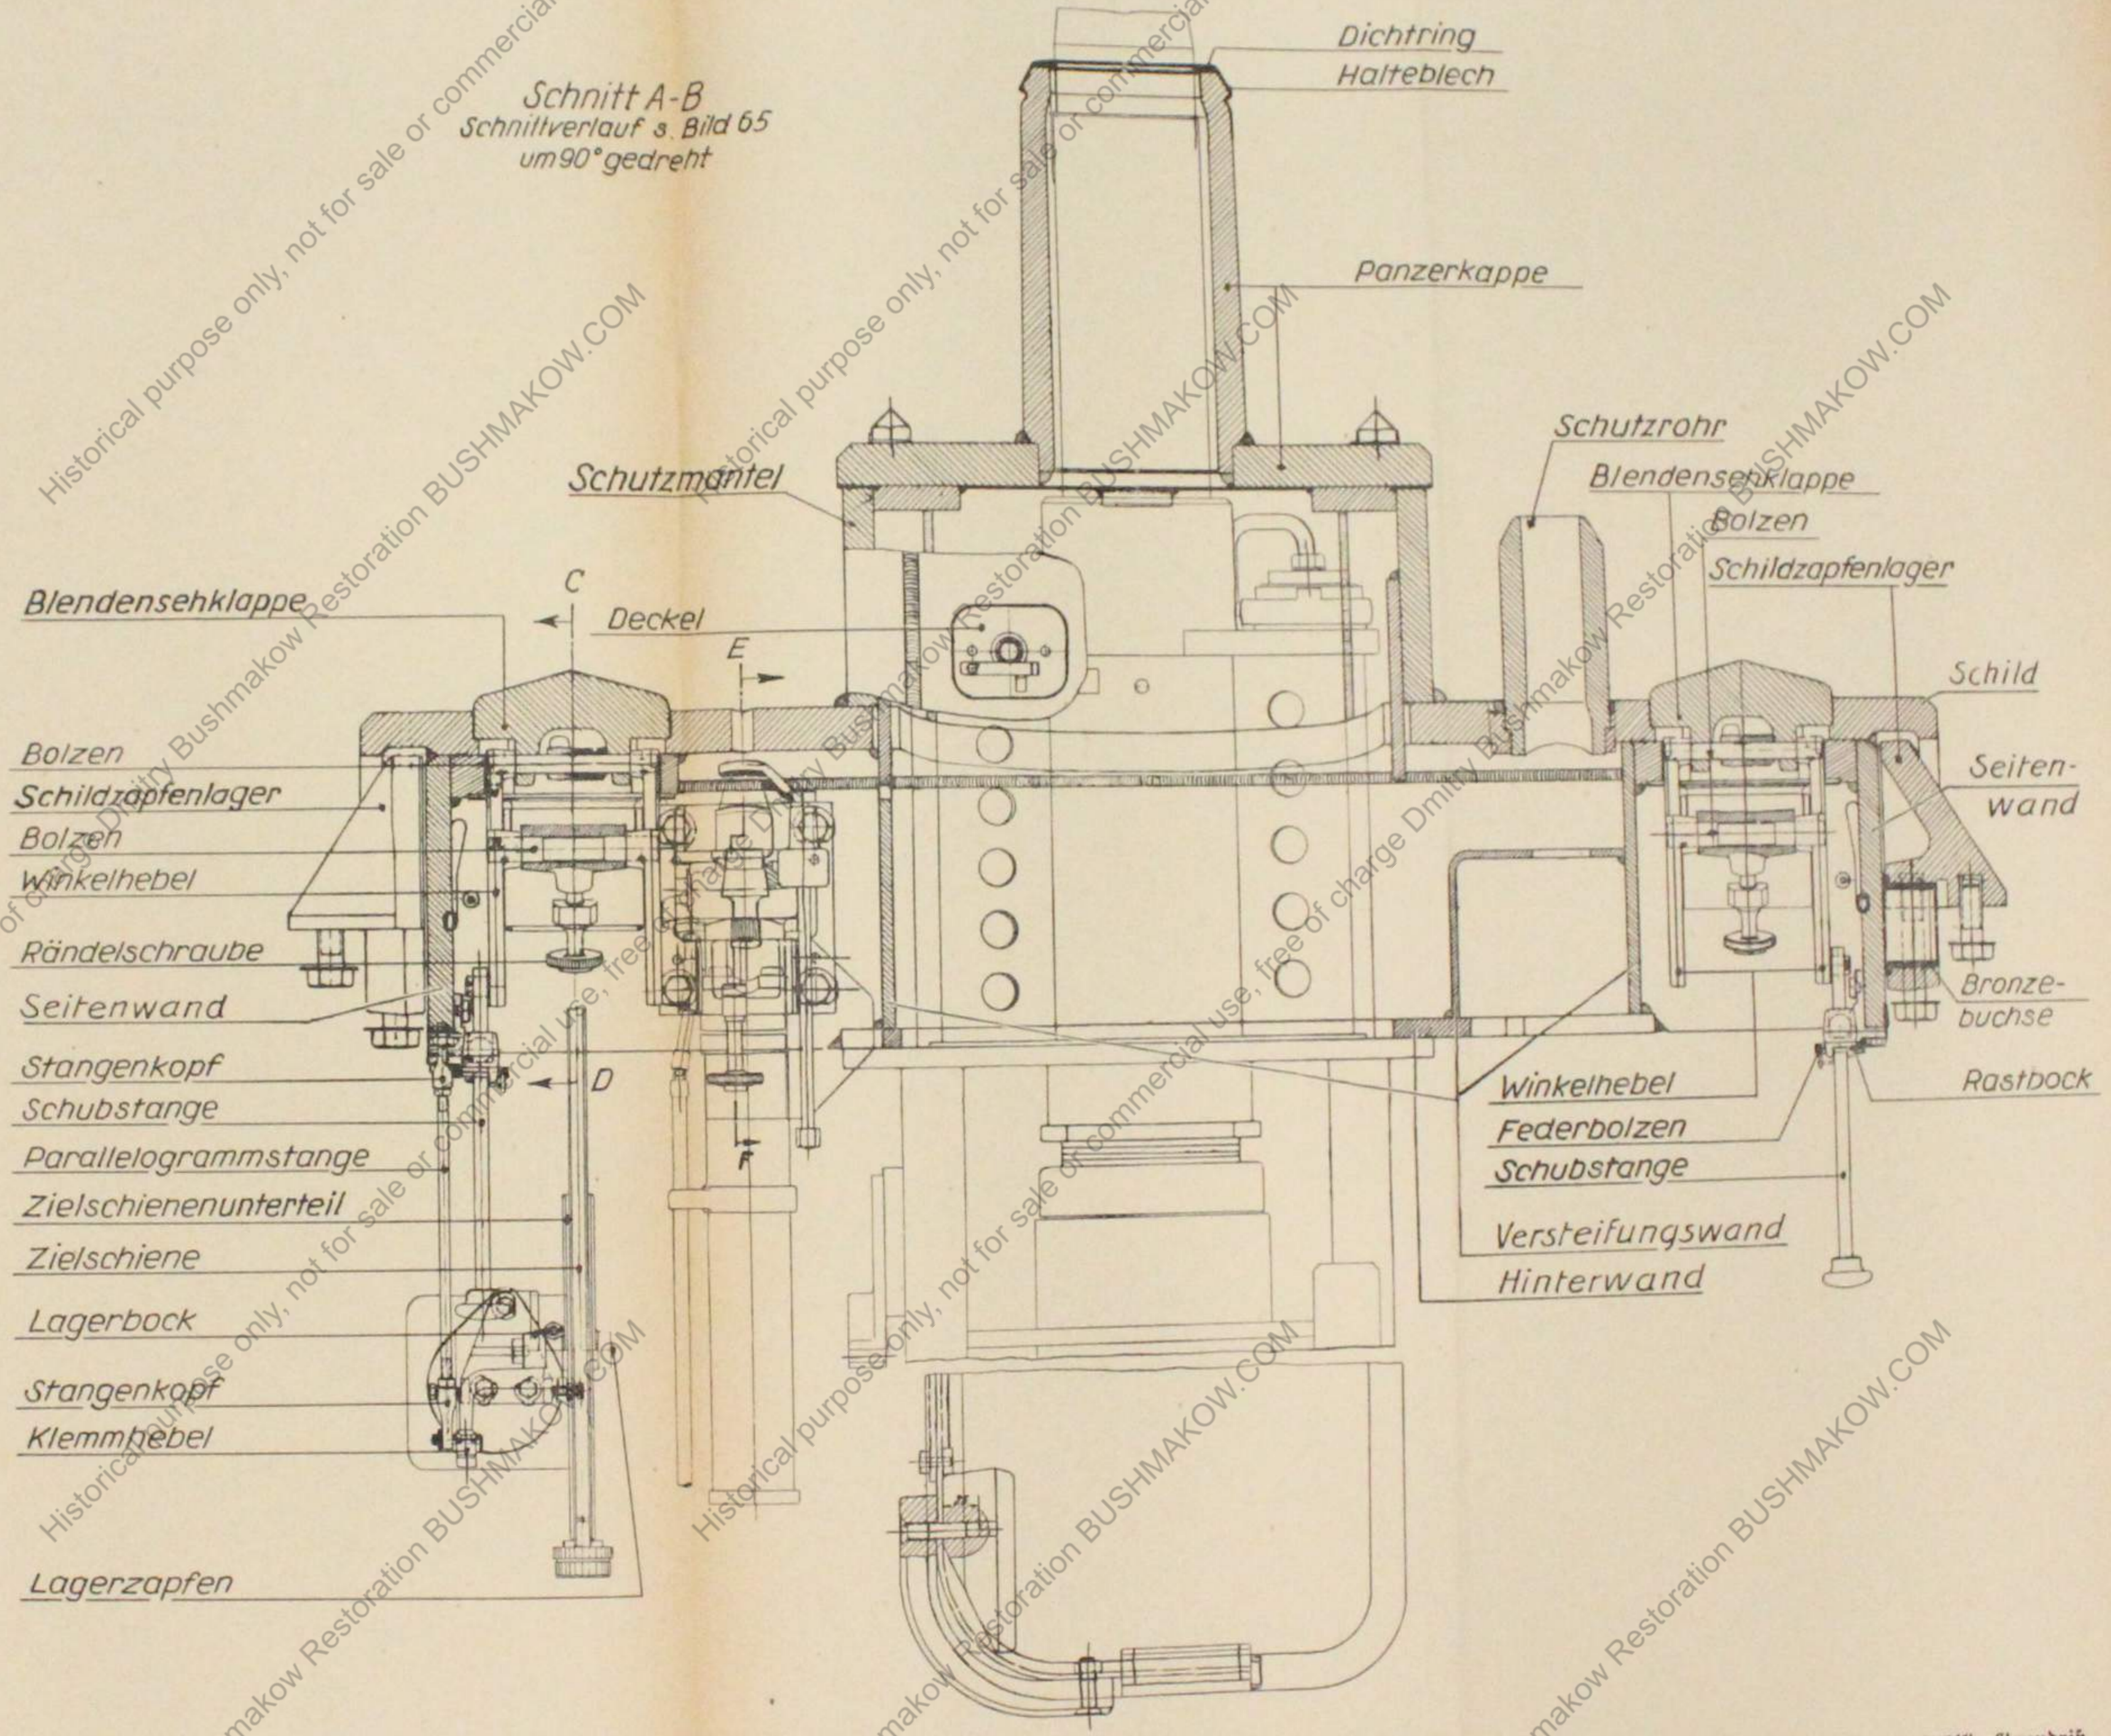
Walzenblende, Ausf. E-H, Schnittbild, Grundriß
